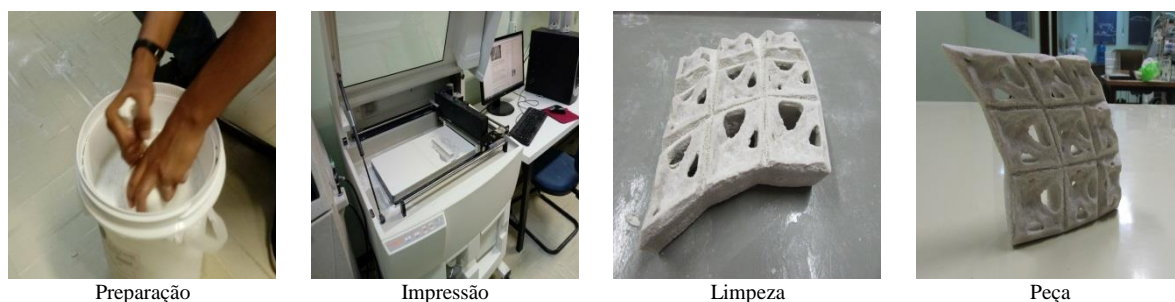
Teste de impressão 3D por fundição de pó de gesso-maltodextrina-açúcar. Fonte: Própria.
